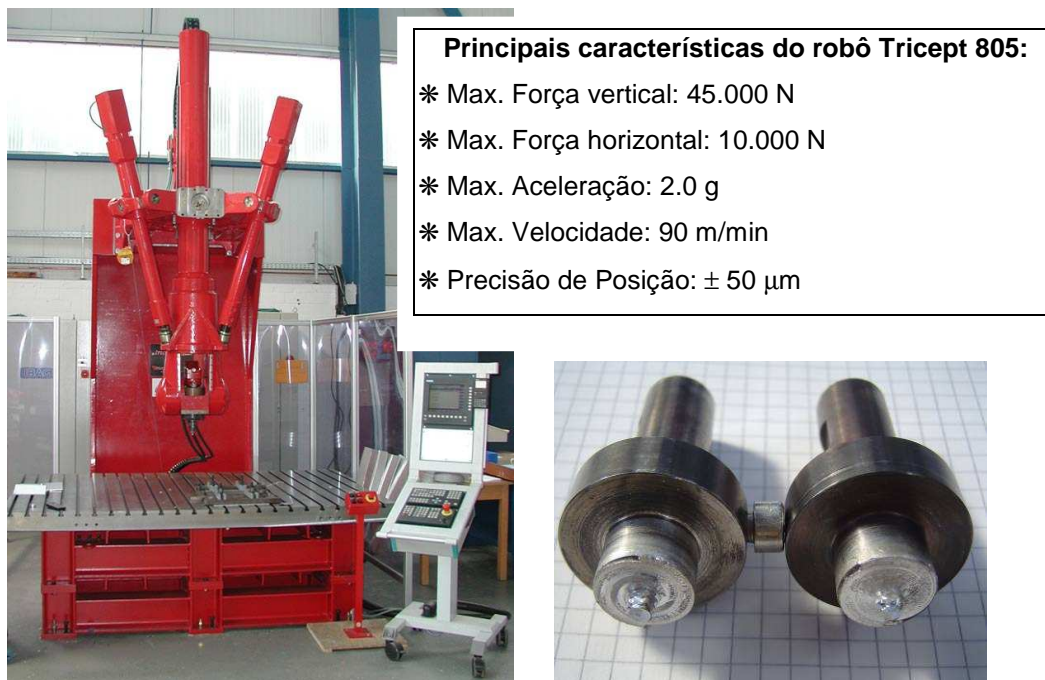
FSW Robô Tricept 805 – controlador Siemens Sinumeric 840D – e a ferramenta utilizada no processo de soldagem – pino facetado com rosca (fonte: GKSS)
